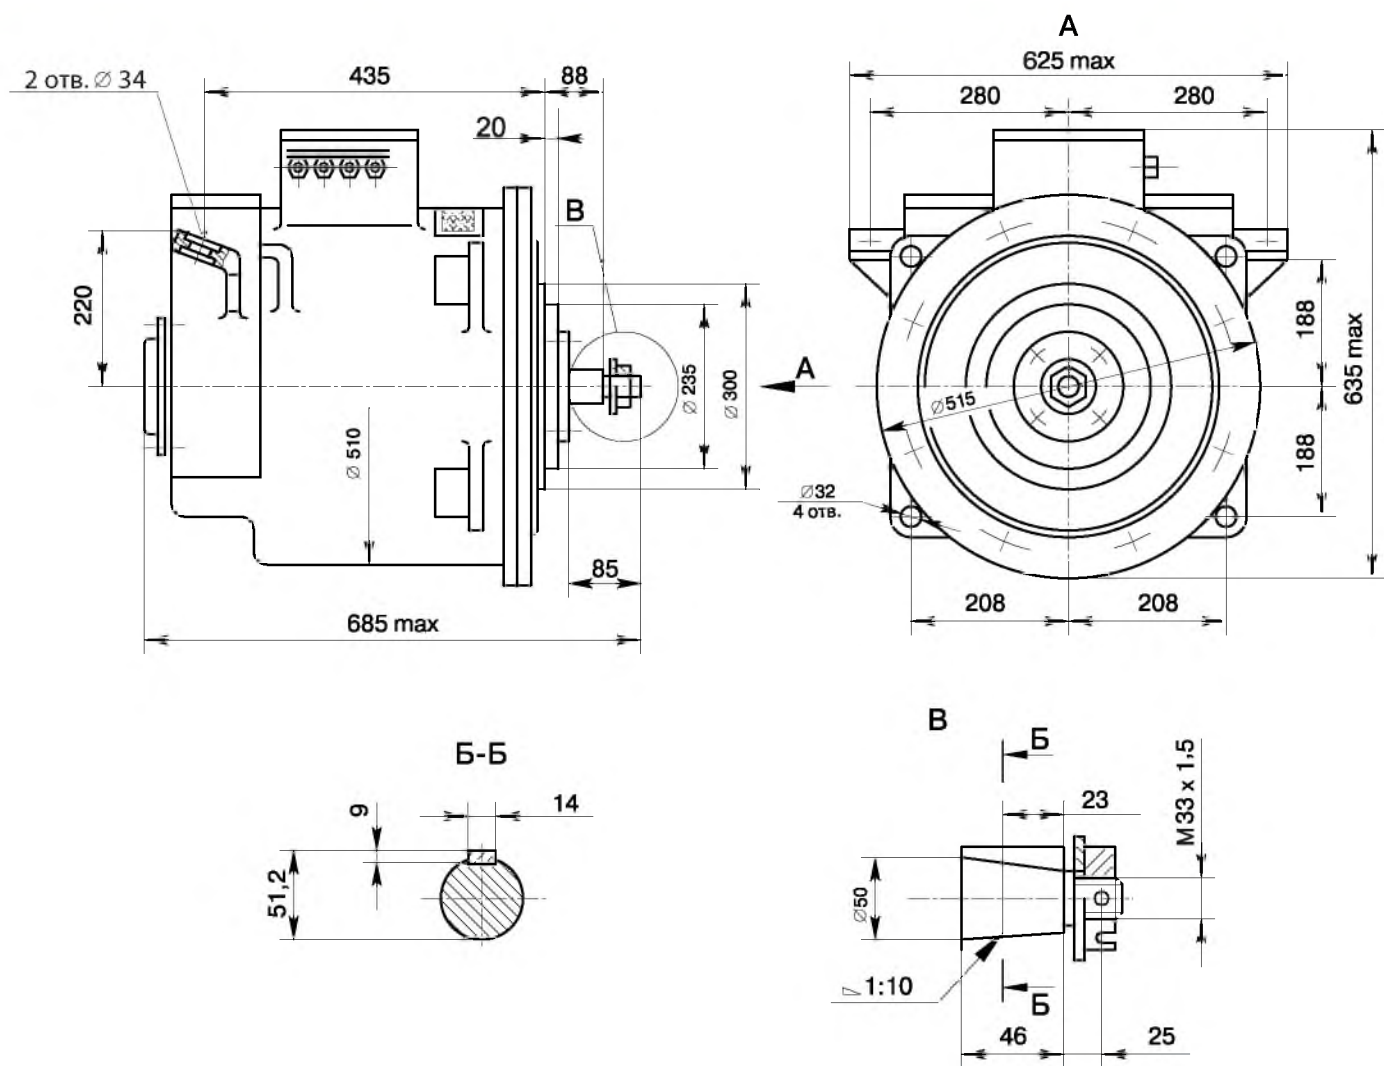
Габаритные и установочные размеры электродвигателя ДТН-33/20
